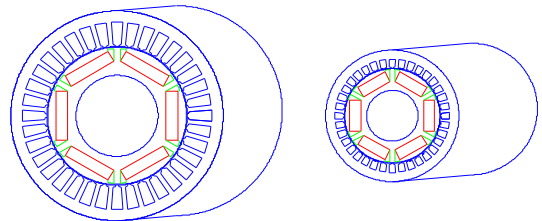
Dimensions de la machine initiale (à gauche) et finale (à droite).
